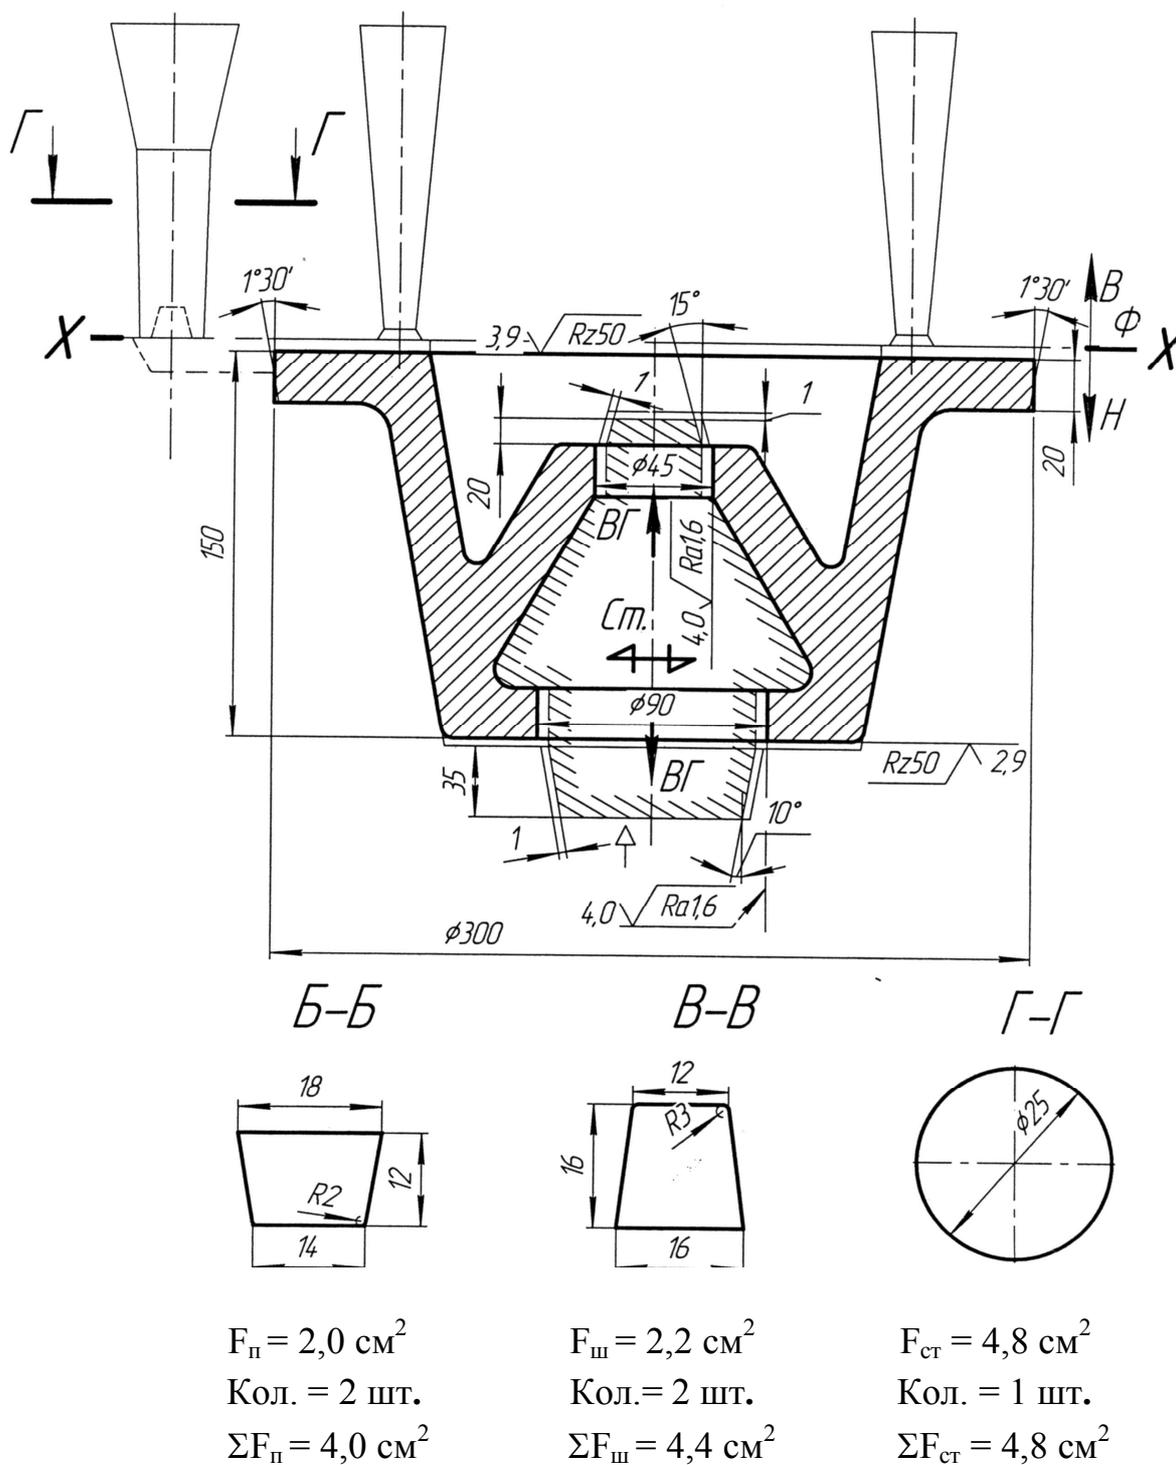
Чертеж детали с элементами литейной формы и отливки
